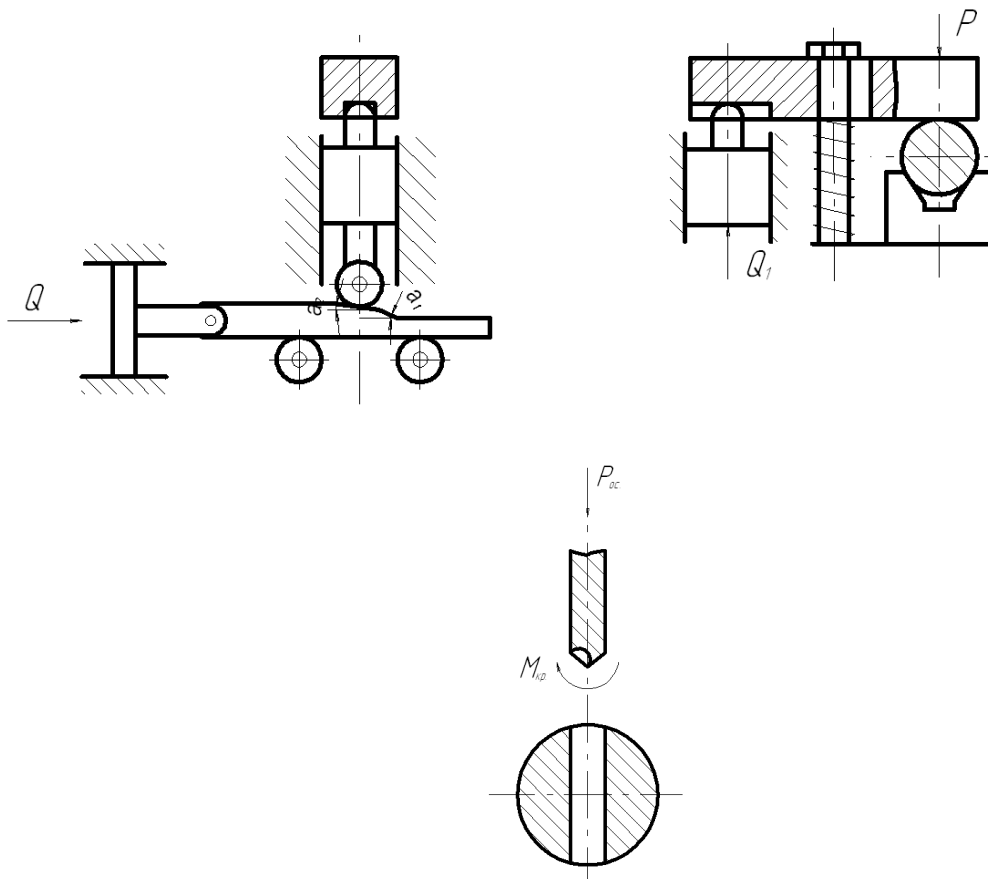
Схема пристосування для кріплення заготовки при свердлінні отвору
